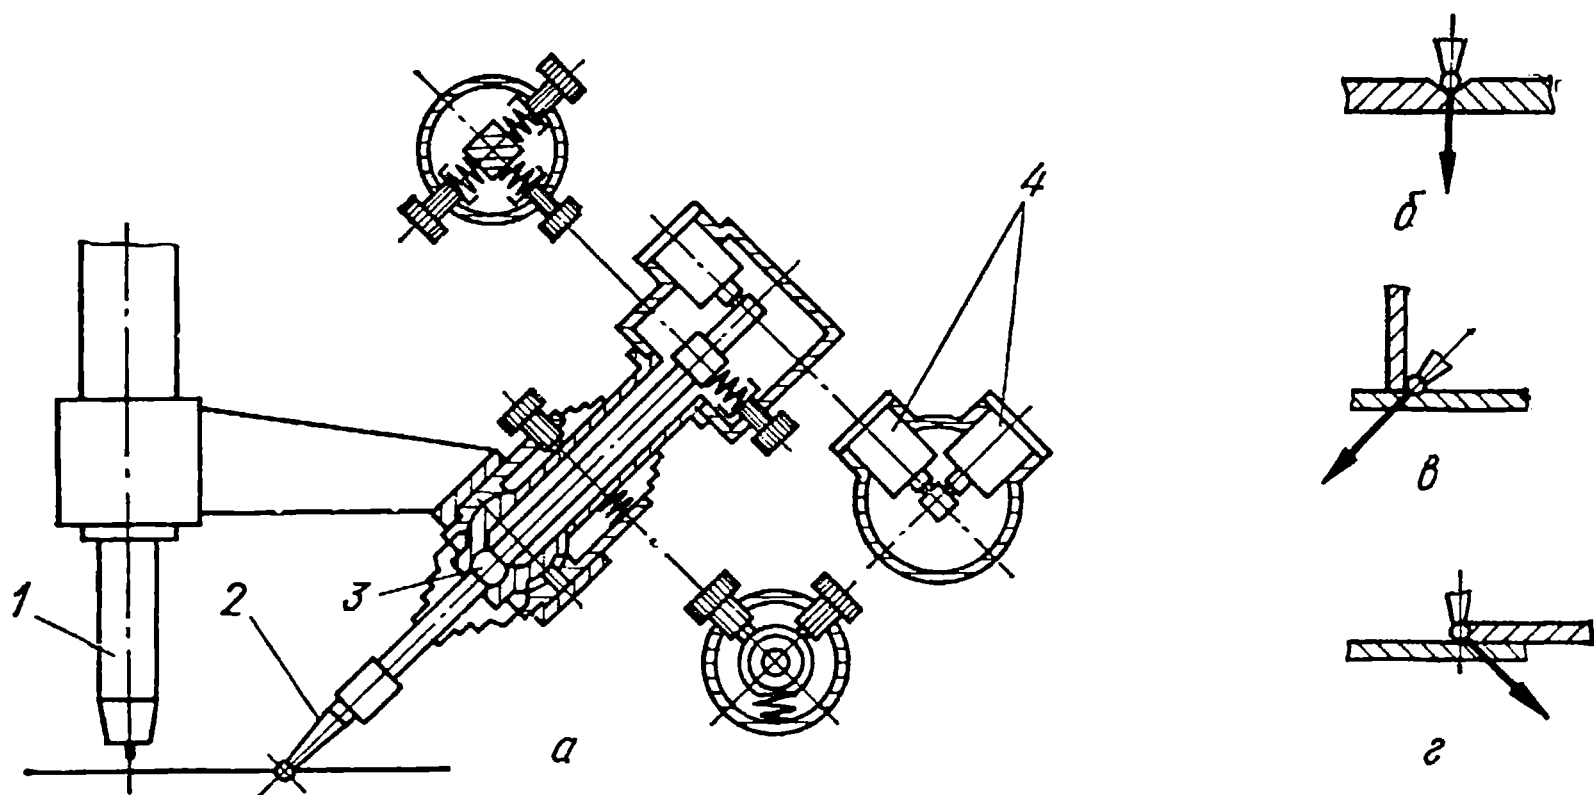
Схема установки двухкоординатного механического датчика (а) и направление результирующего усилия копирования при сварке стыковых (б) и угловых швов (в, г):
